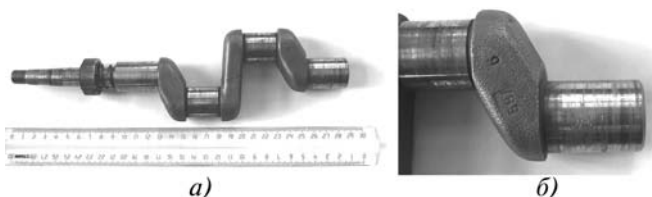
Коленчатый вал компрессора (а) и внешний вид его изношенной шейки (б)
